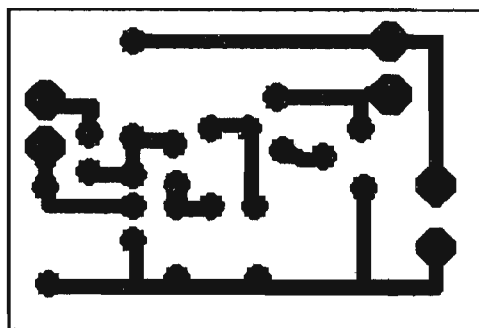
Disegno del circuito stampato 1:1 lato rame.
